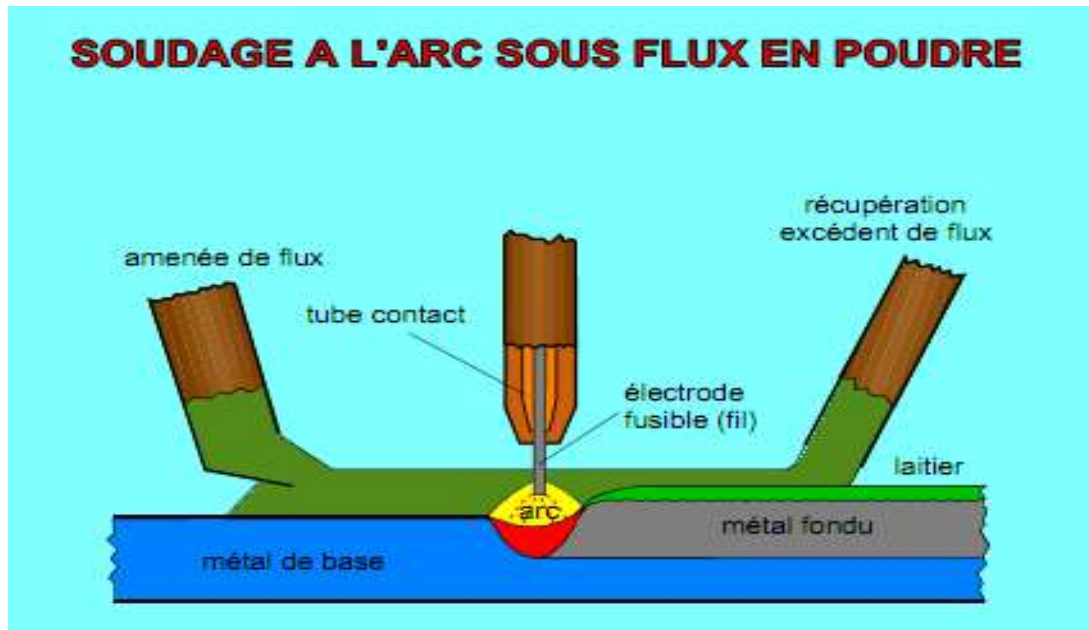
Soudage sous flux en poudre [13].
